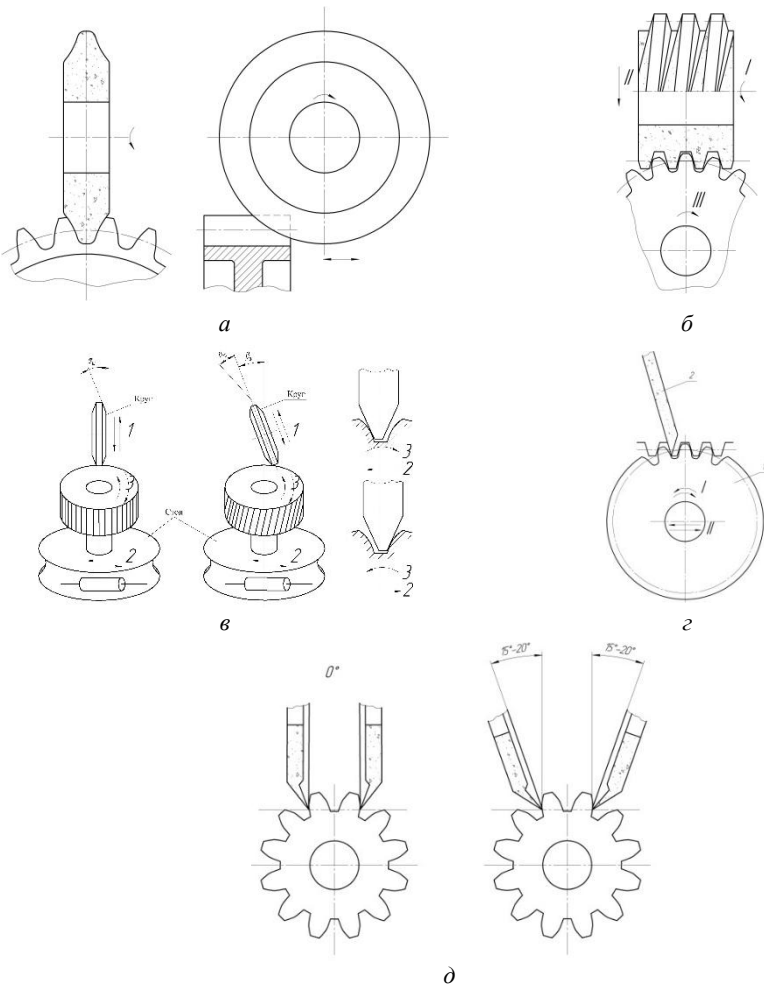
Схемы шлифования зубчатых колес различными методами:
